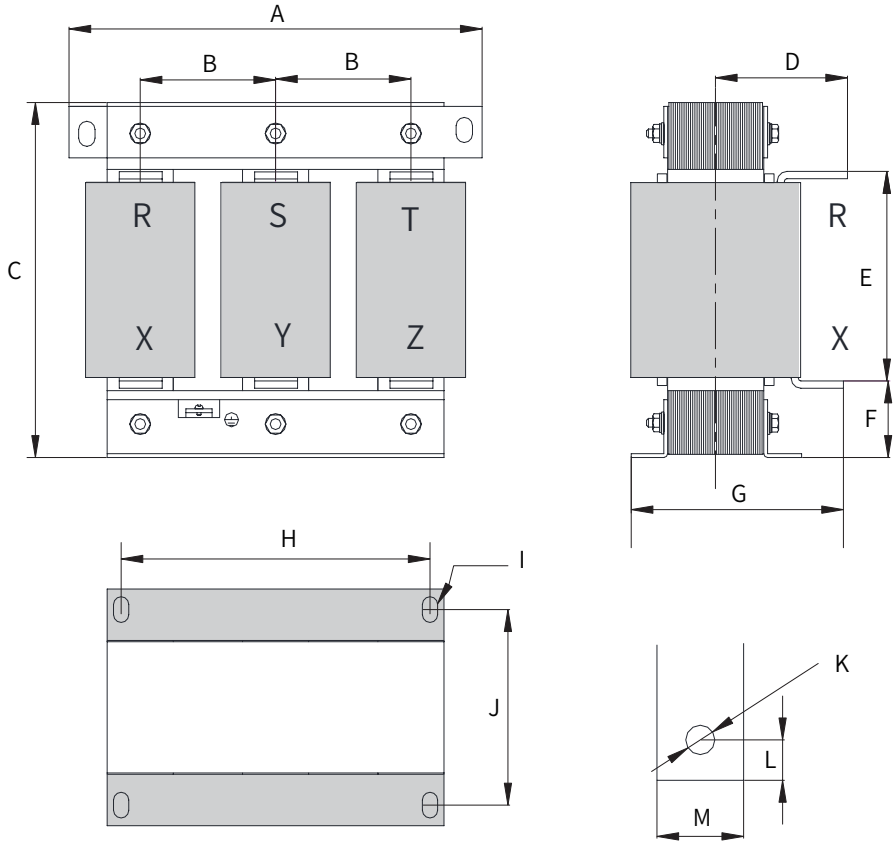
Размеры входного реактора переменного тока 150 - 330 А
